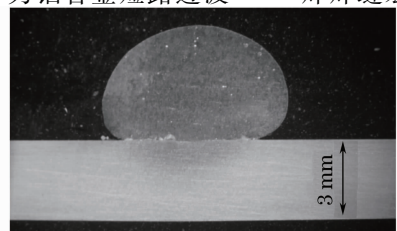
铝合金短路过渡 MIG 焊焊缝宏观形貌
